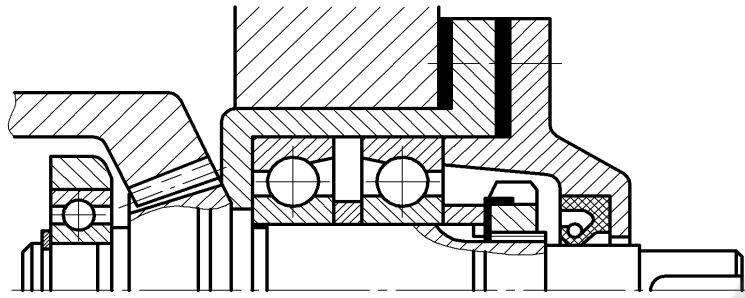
Подшипниковый узел с расположением зубчатого венца между опорами
